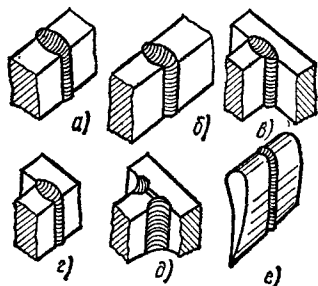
Основные виды сварных соединений, выполняемых электрошлаковой сваркой:
